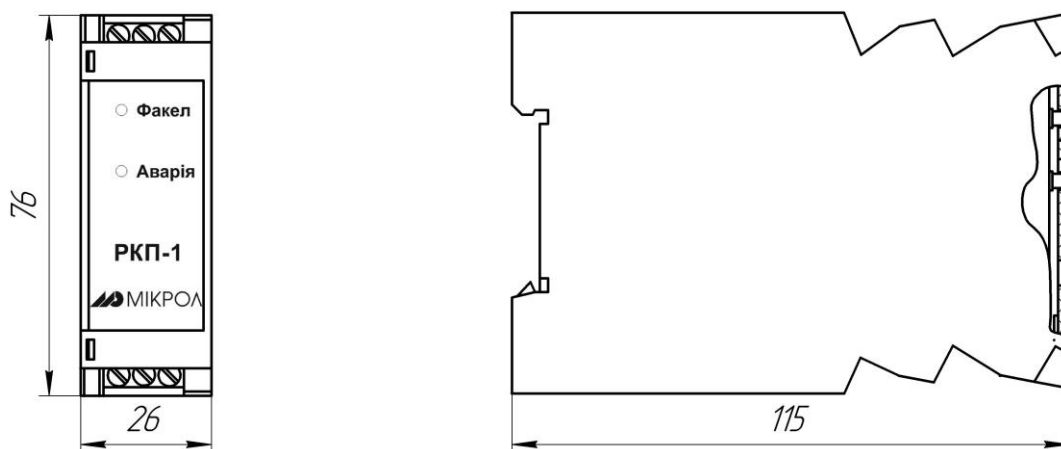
Внешний вид и габаритные размеры РКП-1
